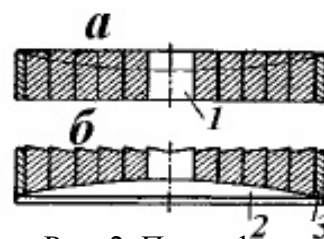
Пресс-форма для пластического формования оптических деталей: а) исходный набор колец; б) готовая пресс-форма для формования линз Френеля: 1 – заглушка; 2 – шаблон; 3 – центрующее кольцо
